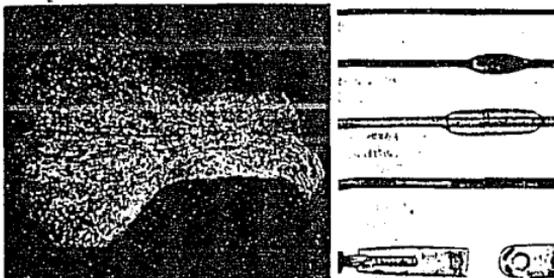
(Izq.) Sección a través de una soldadura en frío.
